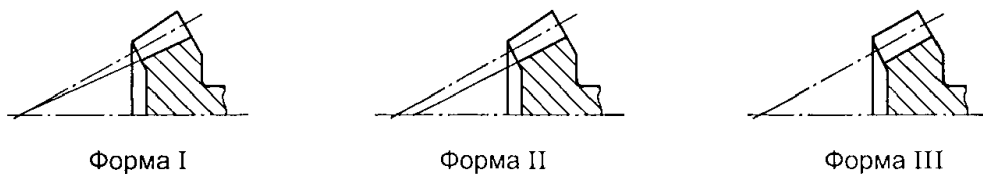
Осевая форма зуба конического зубчатого колеса
